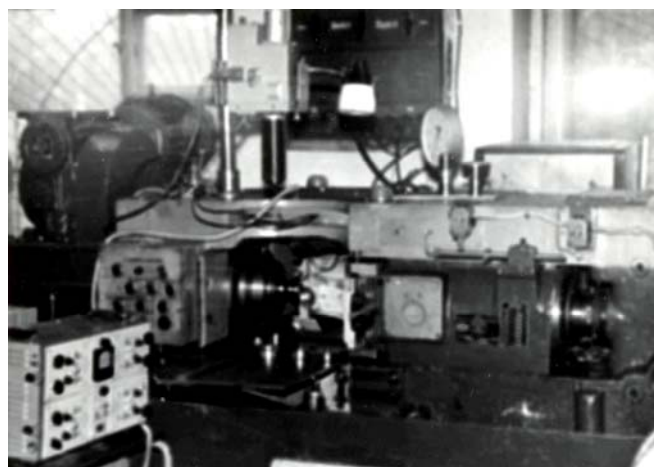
Общий вид станка МРК-30 с коническим раскатным валком, полученного на базе модернизации резьбонакатного станка
